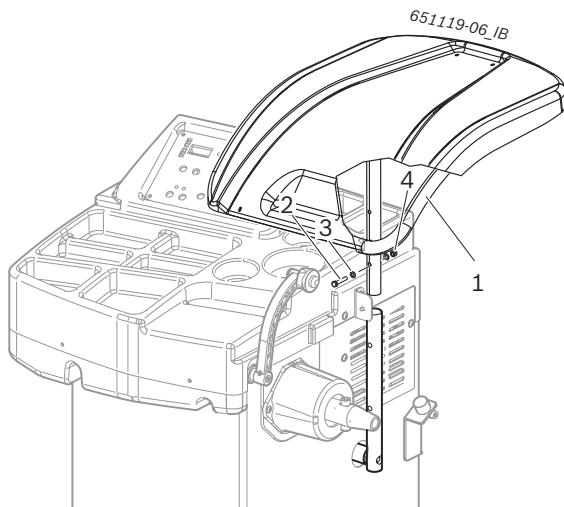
Крепление опорного кронштейна к станку MT 826 / MT 826 D
